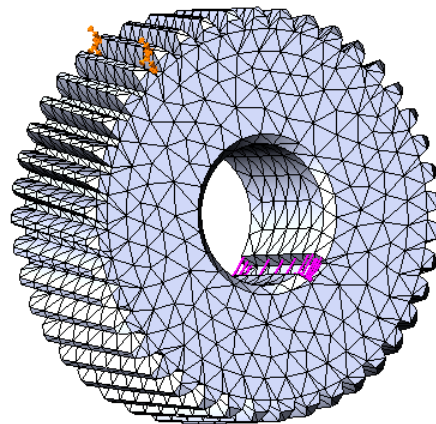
3D-модель циліндричного косозубого редуктора
